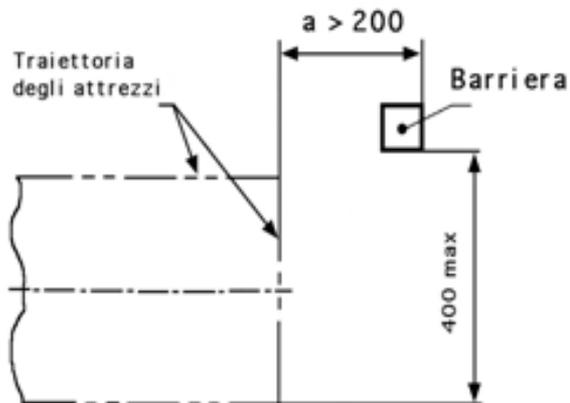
prospetto indicante le distanze di sicurezza delle barriere di protezione dalla traiettoria degli utensili - tratte dalla EN 708
